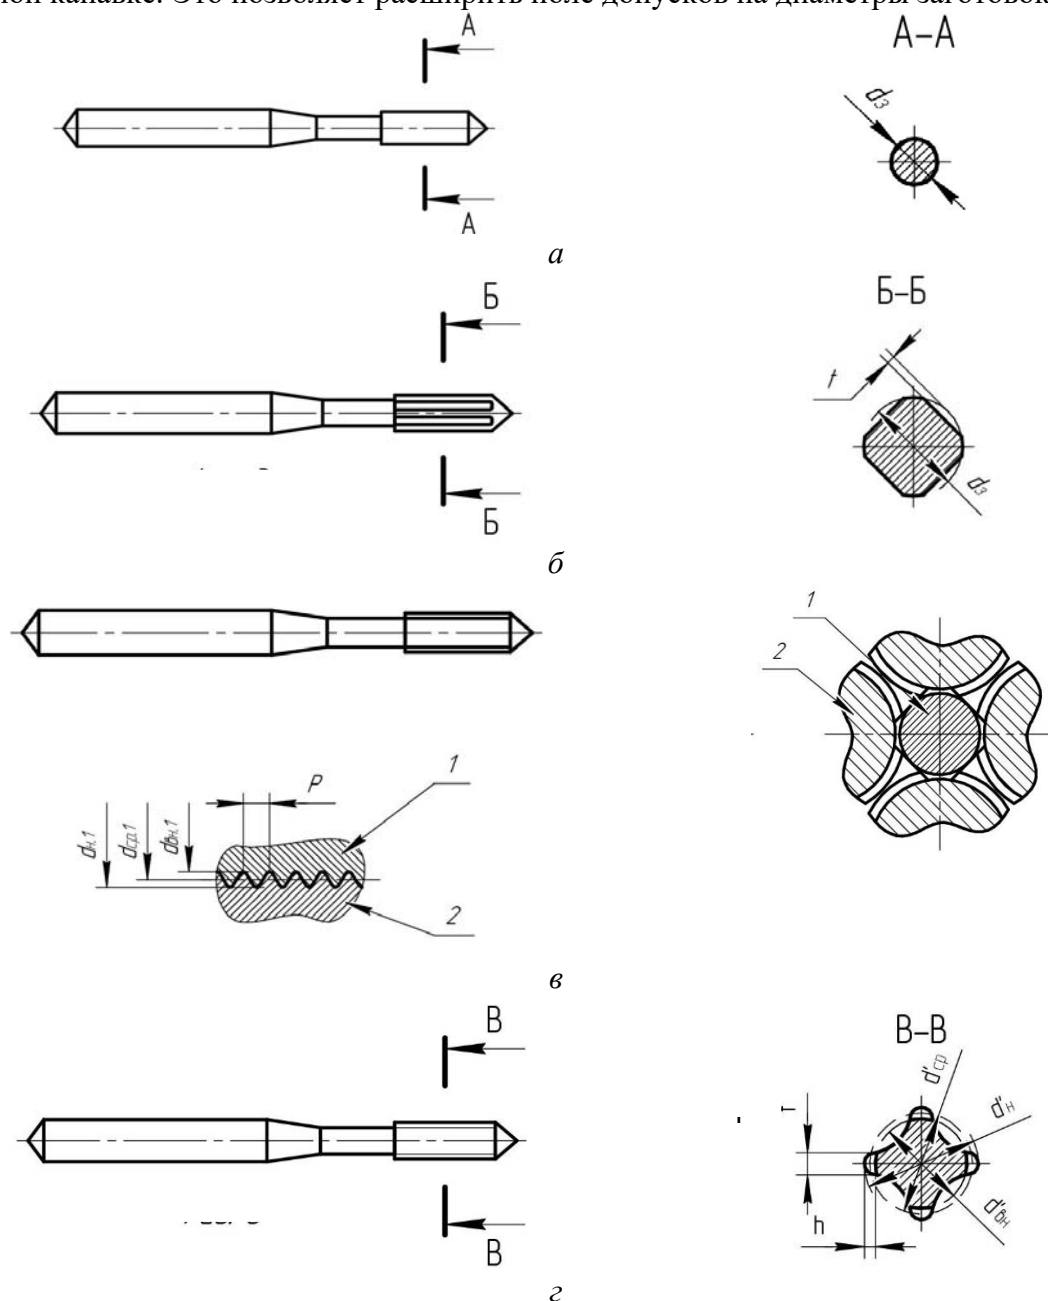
Схема (авт. свид. SU 1340878) формирования метчика: а – заготовка с рабочей частью круглого поперечного сечения А-А; б – заготовка с поперечным сечением в виде правильного
